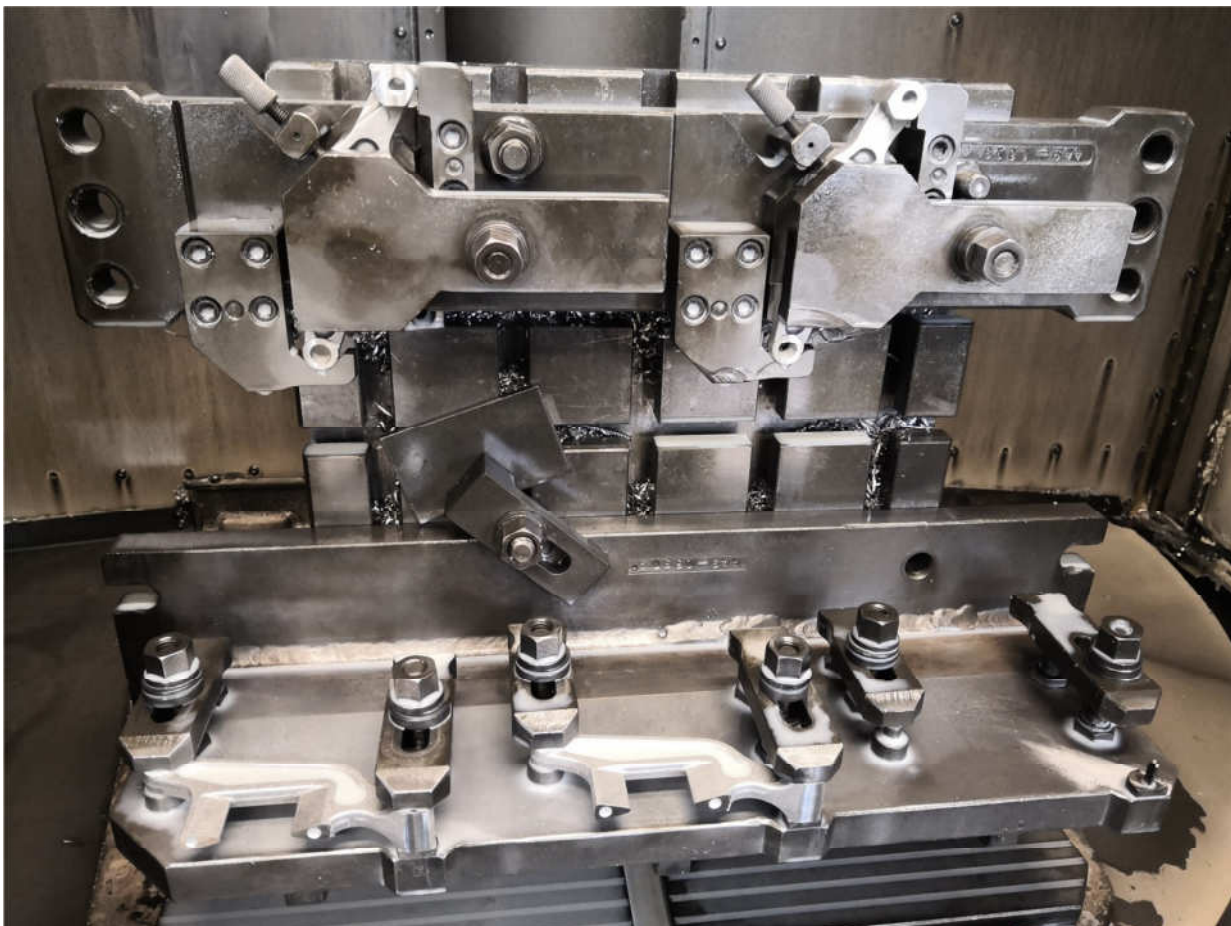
1 CNC stroj TAJMAC-ZPS 500
